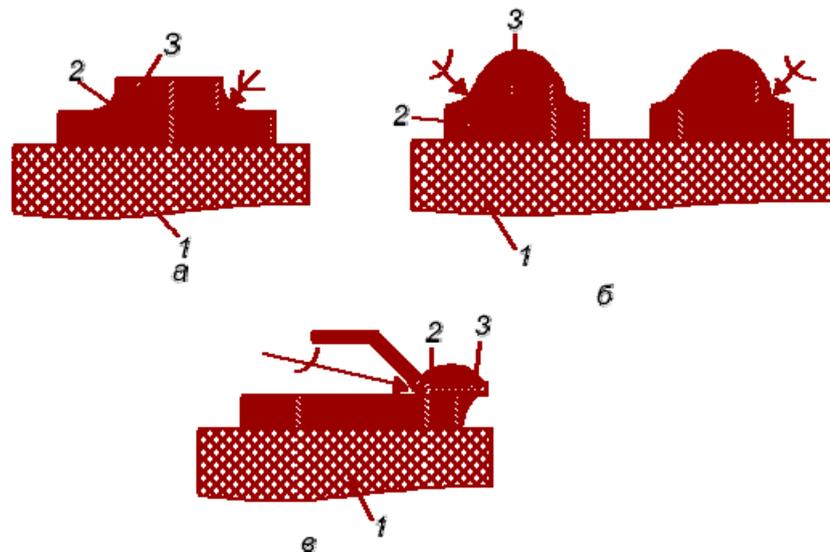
Форма паяных соединений планарных выводов навесных элементов с контактными площадками ПП: 1 – основание платы; 2 – контактная площадка; 3 – планарный вывод
